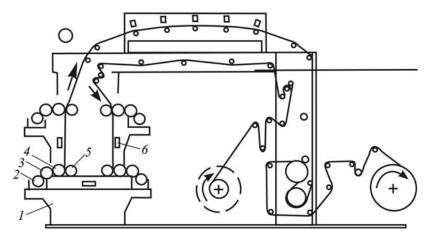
Схема четырехкрасочной флексографской машины: 1 — станина; 2 — краскоподающий цилиндр; 3 — растровый цилиндр; 4 — формный цилиндр; 5 — печатный цилиндр; 6 — сушильное устройство
